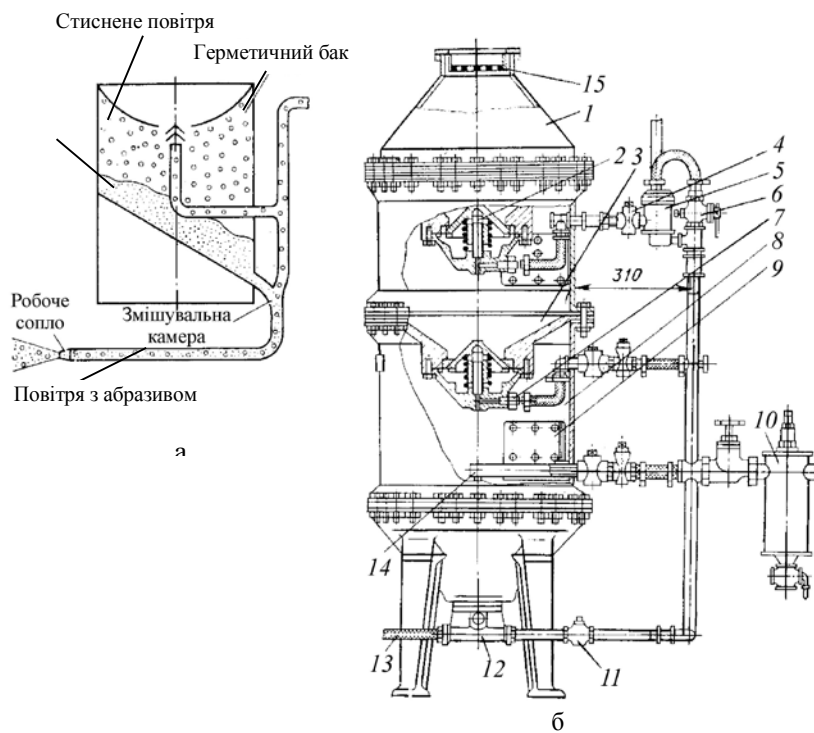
Дробоструминний апарат: а – принципова схема роботи; б – конструкція двокамерного апарата; 1 - верхня камера; 2 - клапан; 3 - середня камера; 4 - сітчастий фільтр; 5 - перемикач; 6 - триходовий кран; 7 - трубка для подавання стиснутого повітря в камери; 8 - нижня камера; 9 - кришка люка; 10 - водовідокремлювач; 11 - запірний кран; 12 - змішувальна камера; 13 - броньований гумовий шланг; 14 - трубка для продування отвору подавання дроби в змішувальну камеру; 15 - сітка
